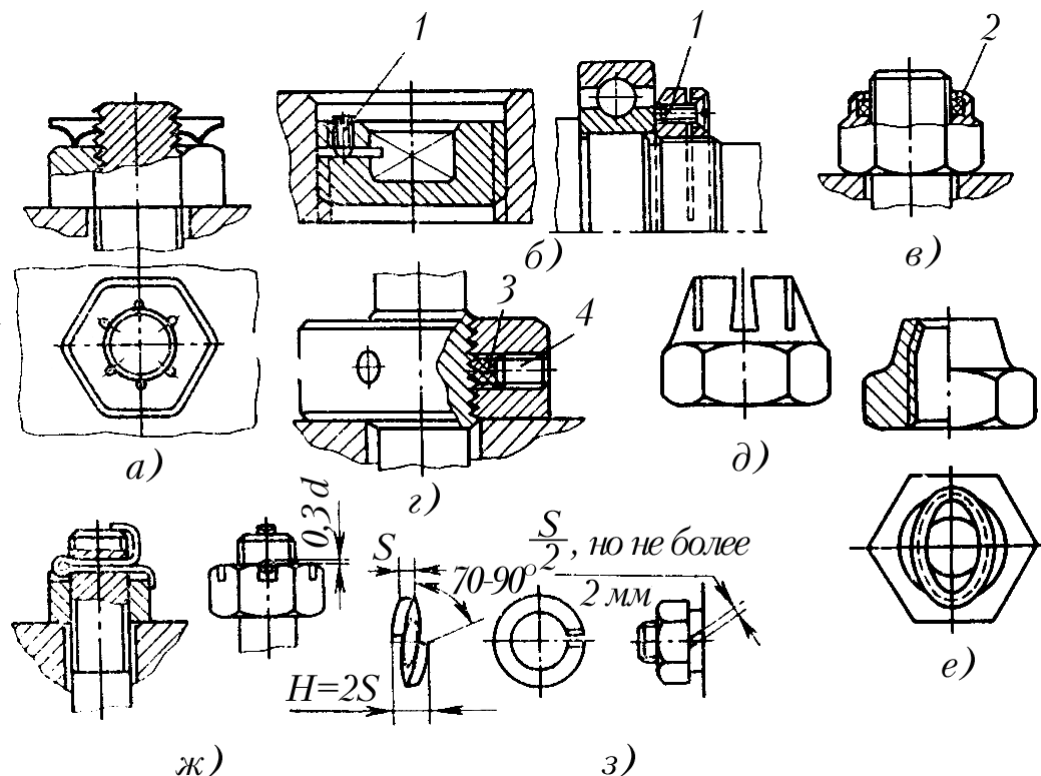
Стопорение резьбовых соединений: (1 и 4 – стопорные винты, 2 – пластмассовая упругая вставка, 3 –алюминиевый шарик).
